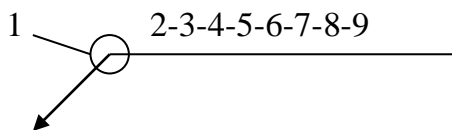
Структура условного обозначения стандартного сварного шва
